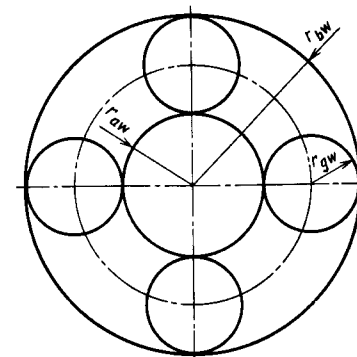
Схема размещения зубчатых колес планетарной передачи
